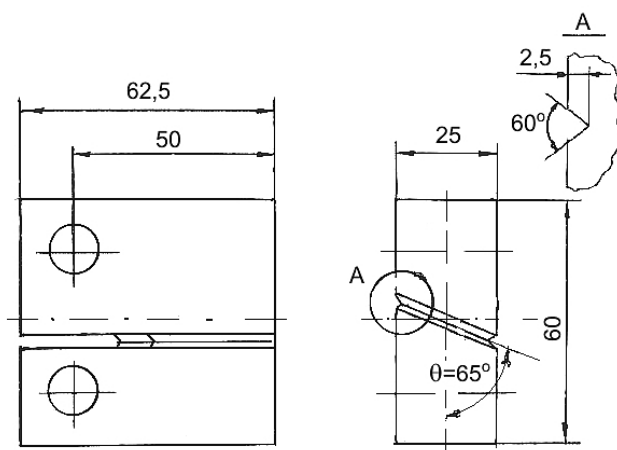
Модернизированный компактный образец с косою трещиной [14].
